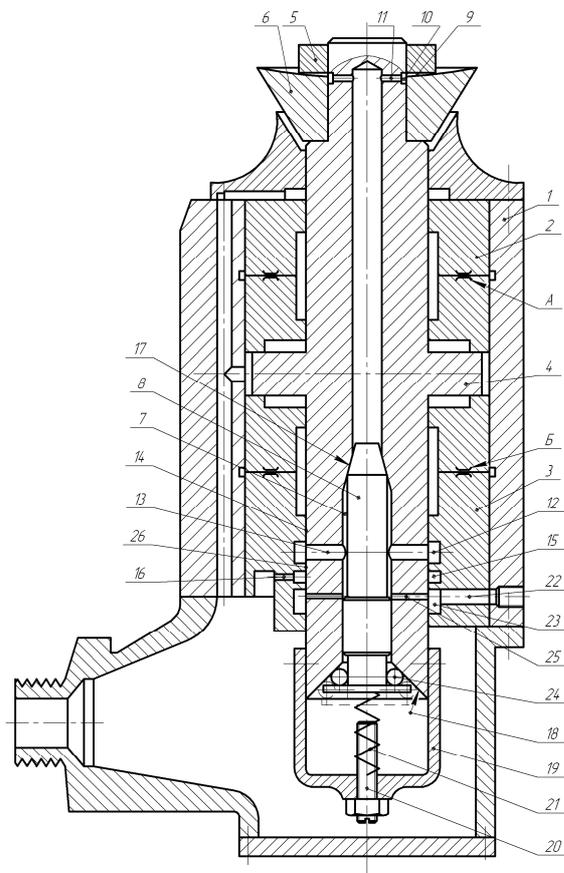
Ротационный резец для высокоскоростной токарной обработки нежестких валов
